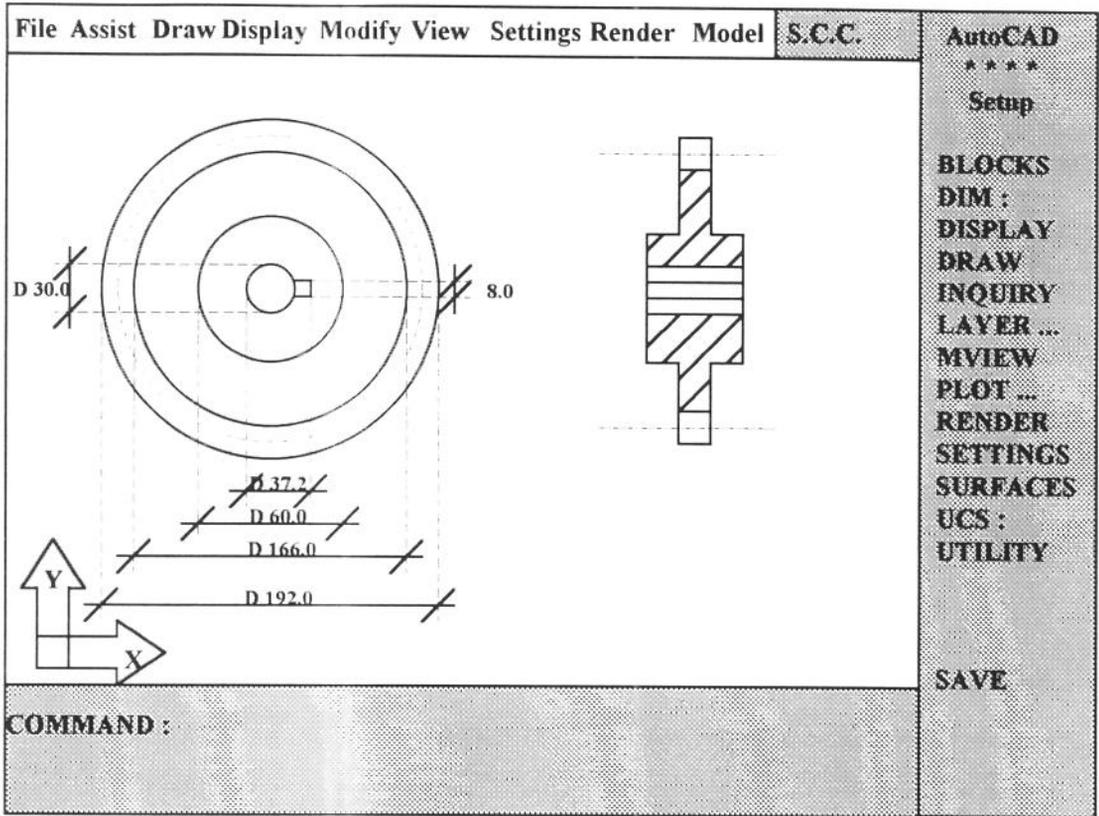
Construção do Corte Transversal - Parte Inferior
